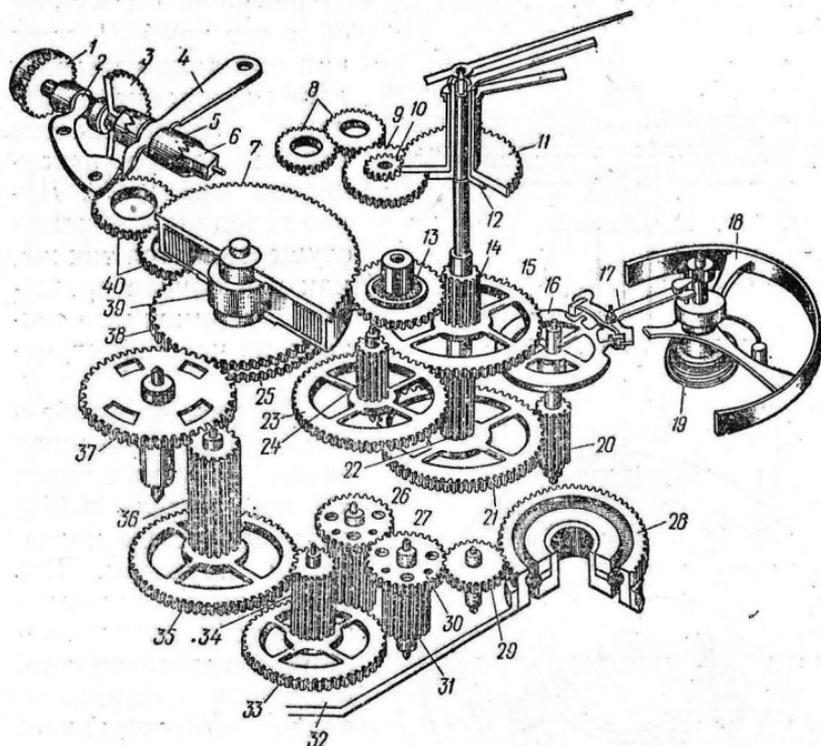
Кинематическая схема часов нормального калибра с автоматическим подзаводом пружины на шарикоподшипниках:
